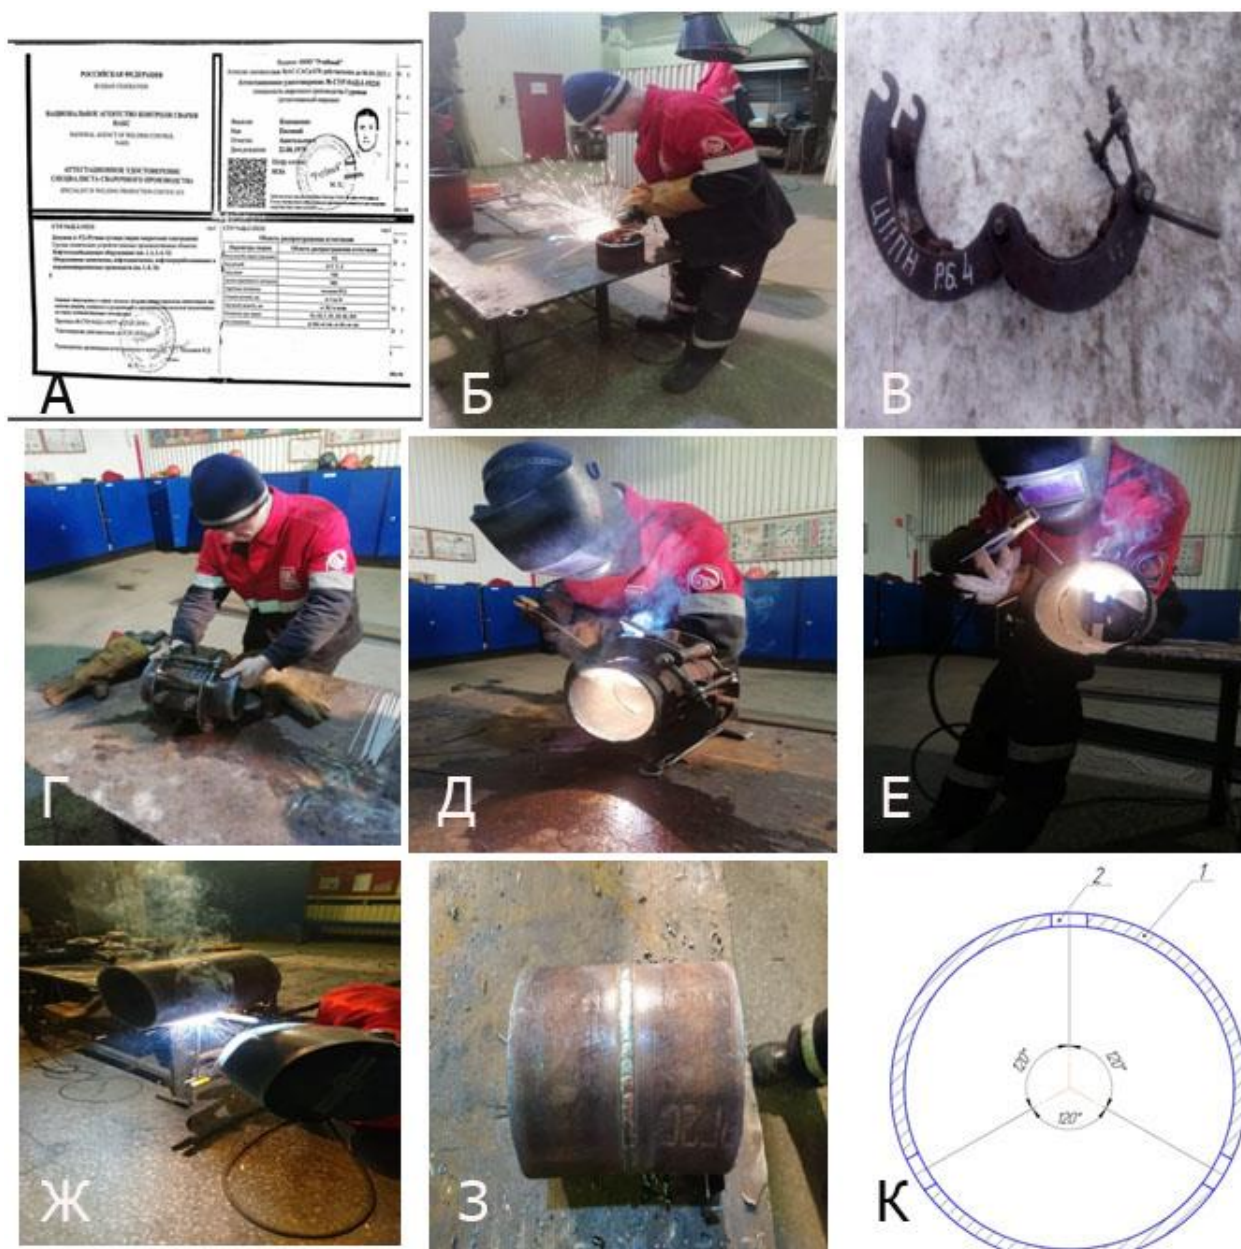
Этапы подготовки образцов для проведения исследования макрошлифов: а – квалификационное удостоверение НАКС сварщика; б – подготовка кромок под сварку; в – внешний вид центратора; г – сборка сварного соединения в центраторе; д – выполнение прихваток; е – сварка корневого шва; ж – сварка заполняющего и облицовочного шва; з – внешний вид заваренных катушек; к - схема вырезки образцов из трубы (материал 09Г2С) для проведения механических испытаний: 1 – изделие; 2 – вырезанный образец
